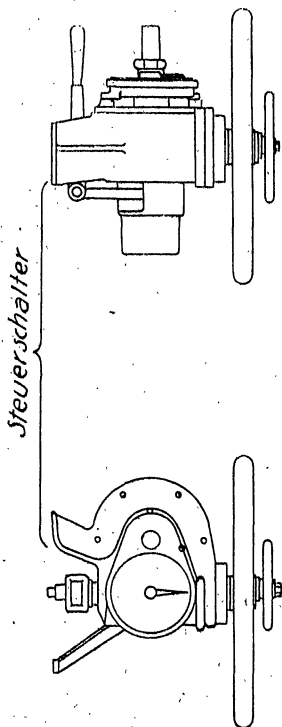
b u. c. Steuerstand für Rudermaschinen mit unmittelbarer Fernsteuerung der Germaniaerft Kiel
